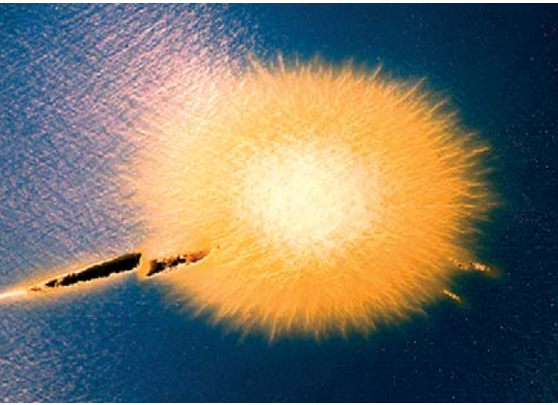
Bruchfläche in einem PE-100-Rohr nach äußerer Punktbelastung (Prüfserie 6).
